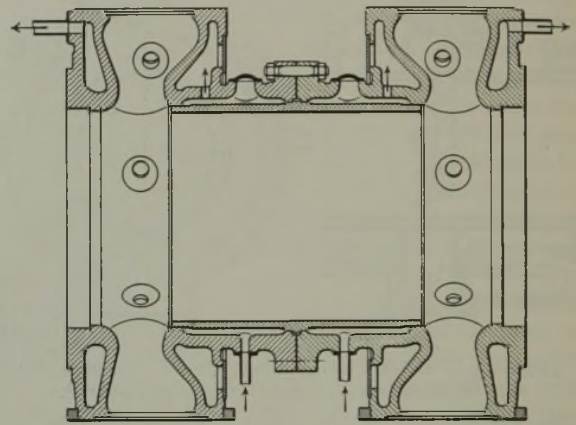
Mehrteiliger Gaszylinder mit unmittelbar gekuhlter Laufbuche; Patent Demag.
